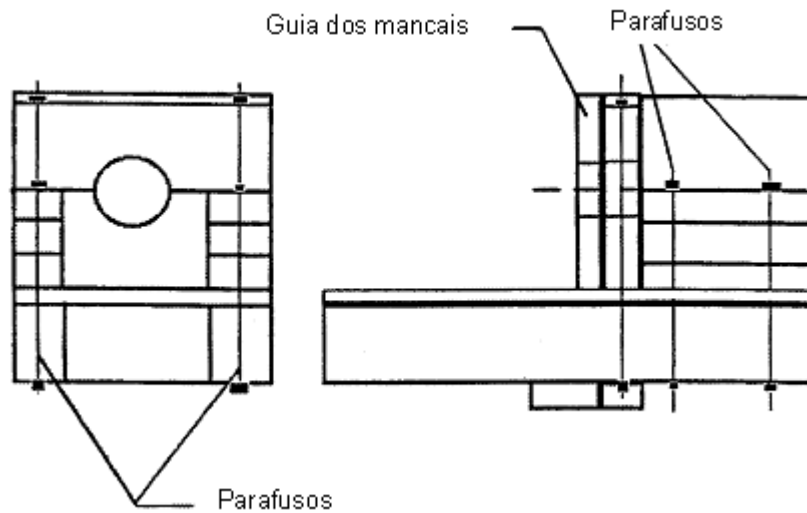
Execução de caixa, reforçada (acima de 15 t)
